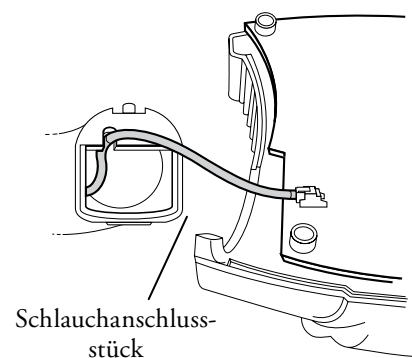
Entfernen des Schlauchanschlussstücks aus dem Erwärmungsgerät.
